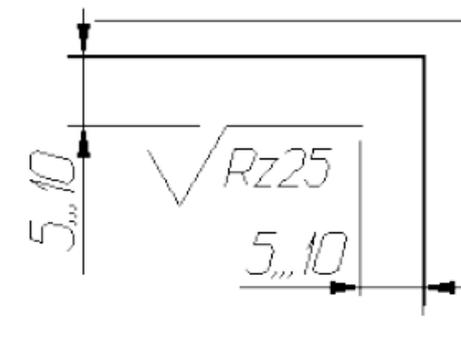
Указание шероховатости одинаковой для части поверхностей изделия
